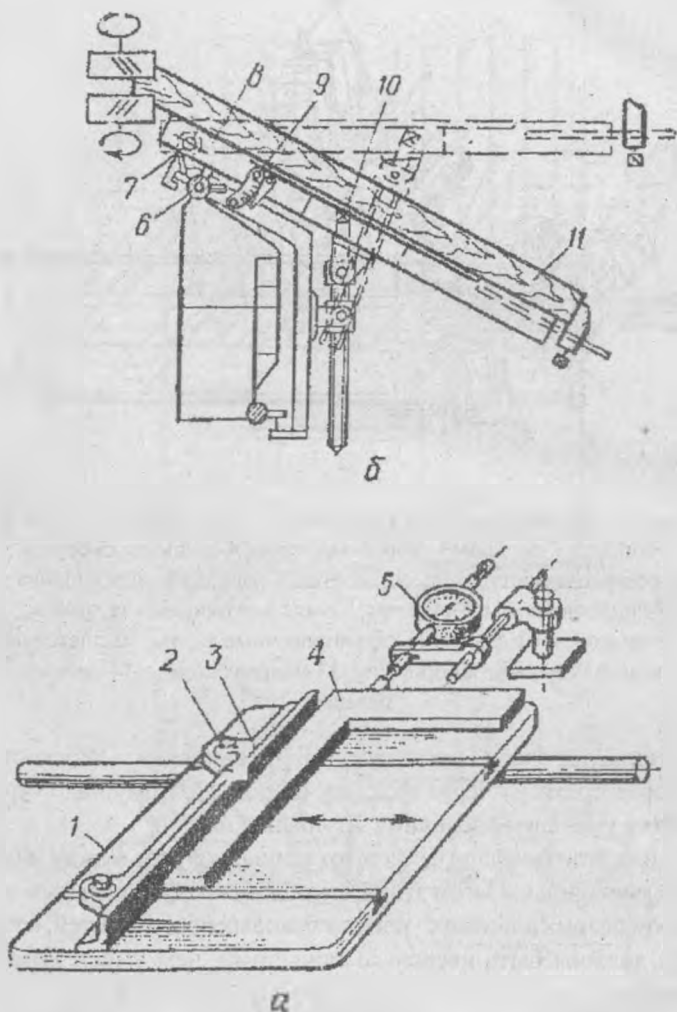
Настройка каретки одностороннего шипорезного станка:
